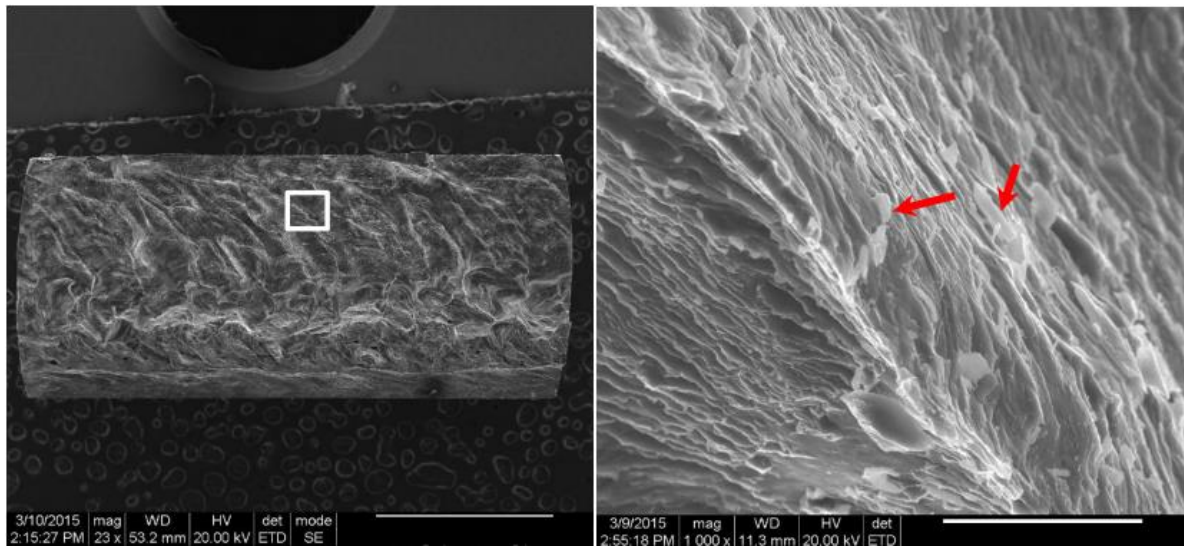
Fractografía mediante MEB de la muestra soldada con 1400 rpm y 500 mm/min a temperatura ambiente (37).
